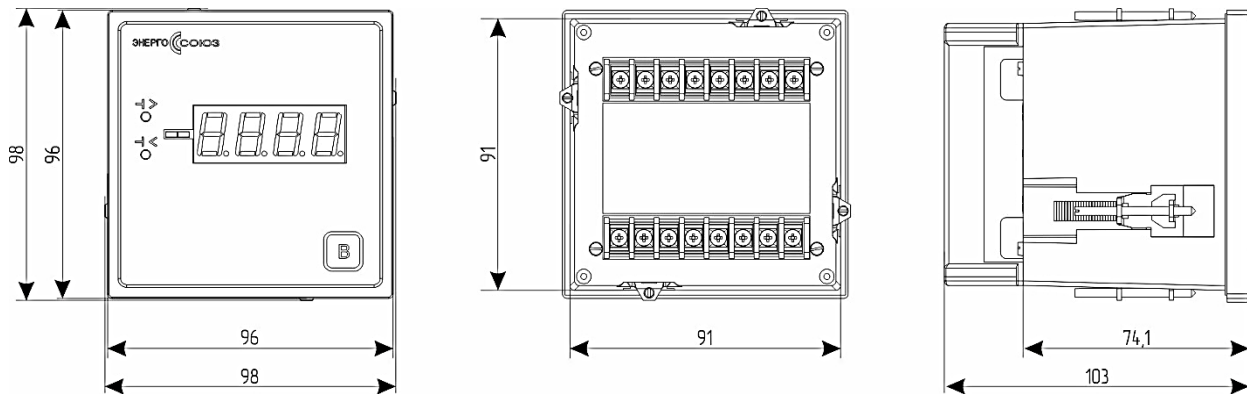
Габаритные и установочные размеры конструктивного исполнения TE
